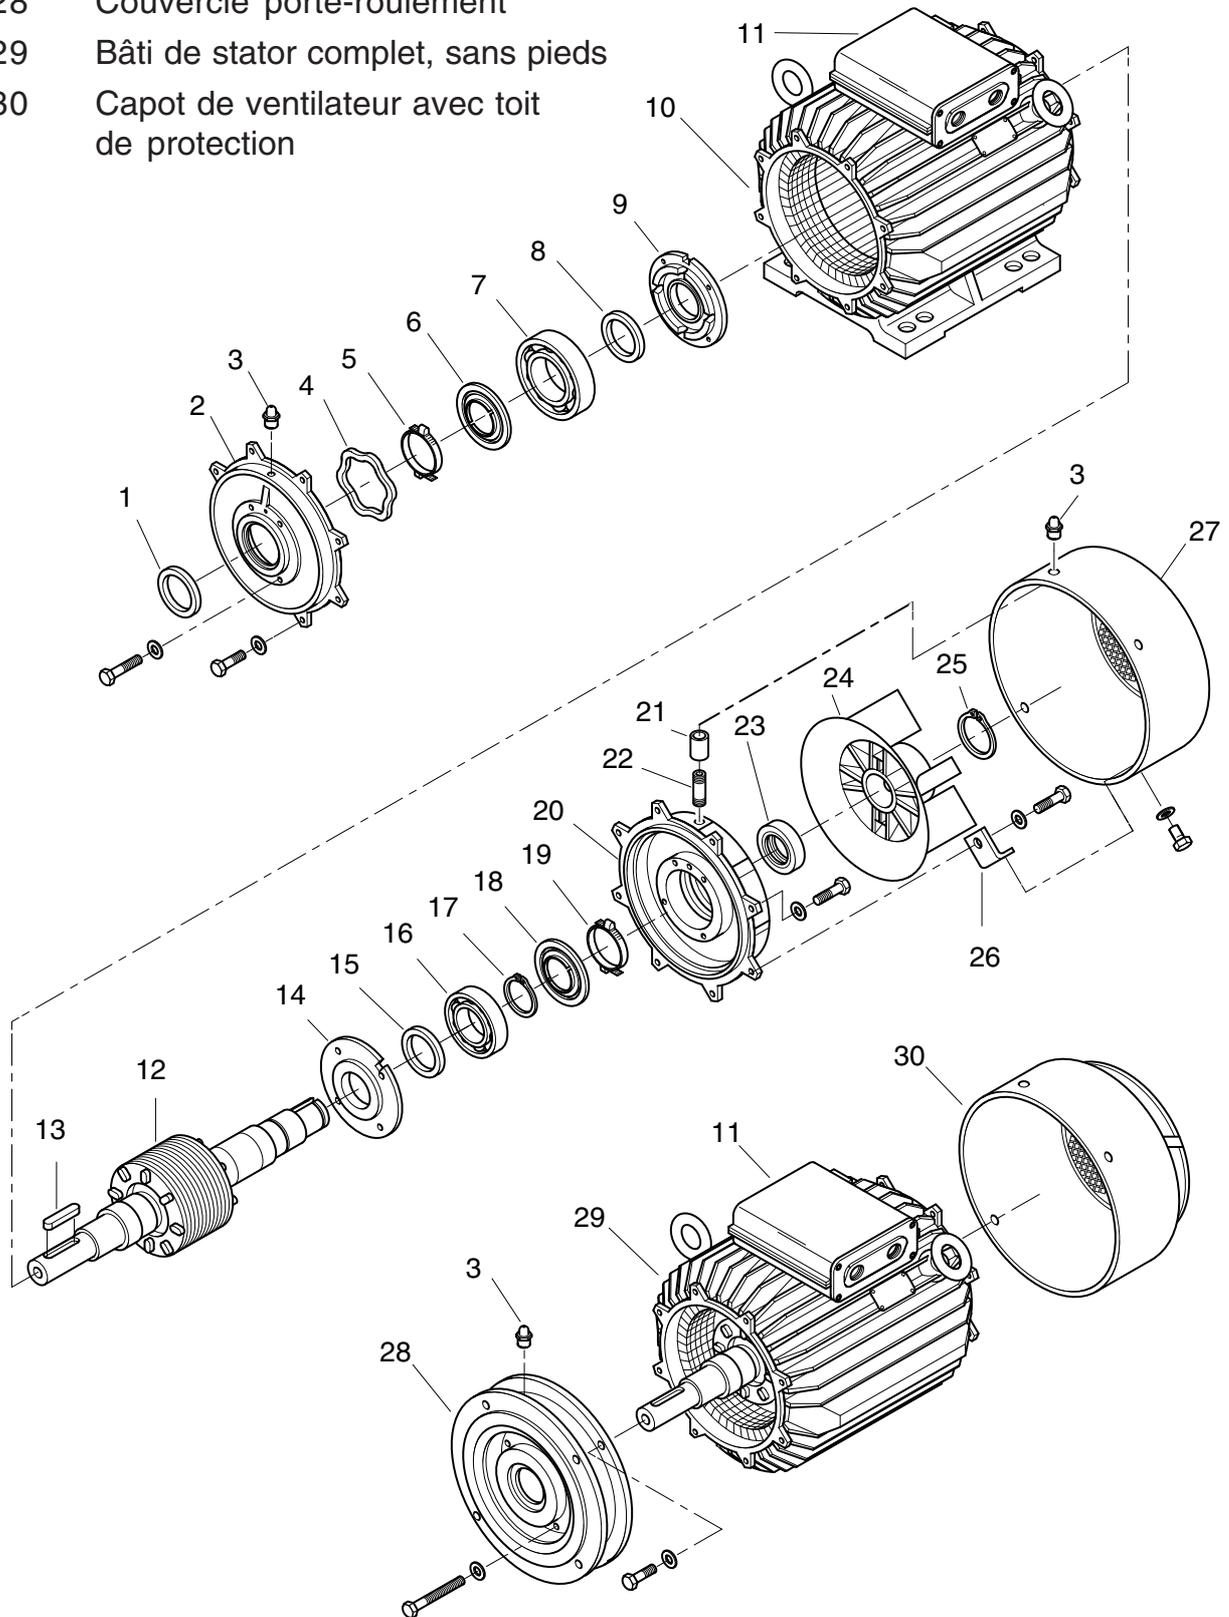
représentation explosée, IP55, Dimension 180M-315L
